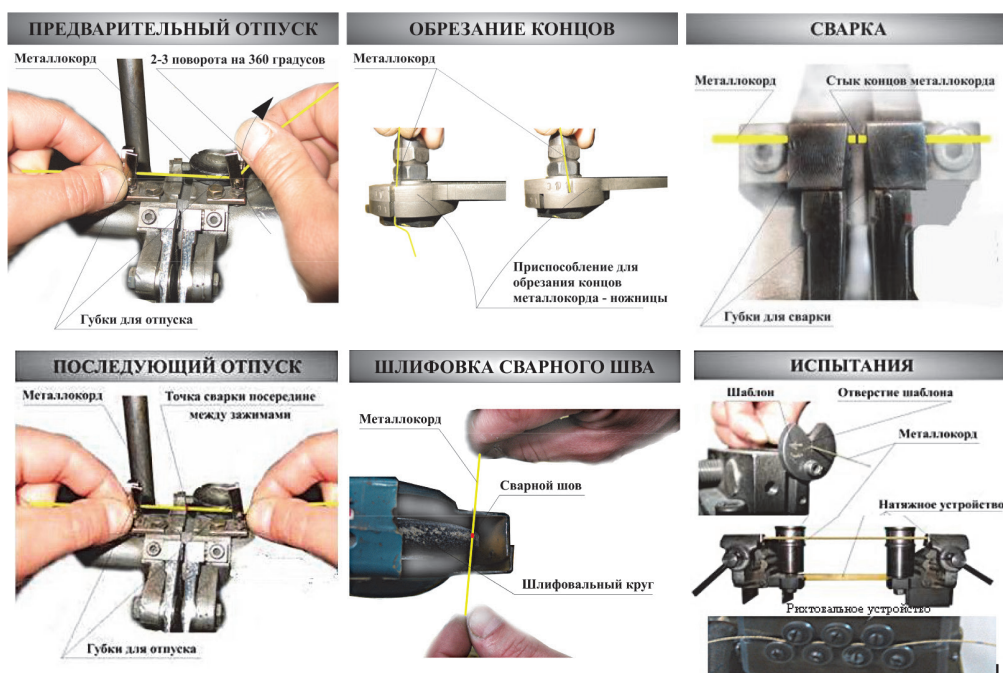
Регламент выполнения сварного соединения металлокорда
